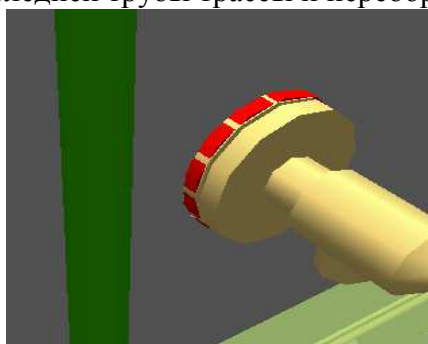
Трасса проходит через непроницаемую конструкцию корпуса
